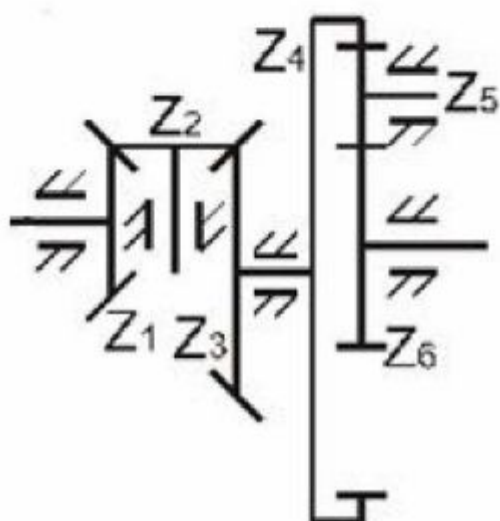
Многоступенчатая зубчатая передача с паразитными колесами
